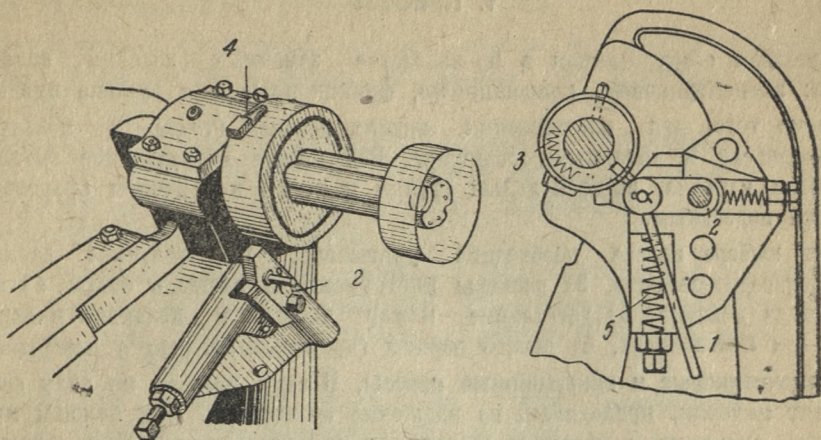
Пусковой механизм прессы с поворотной шпонкой.
